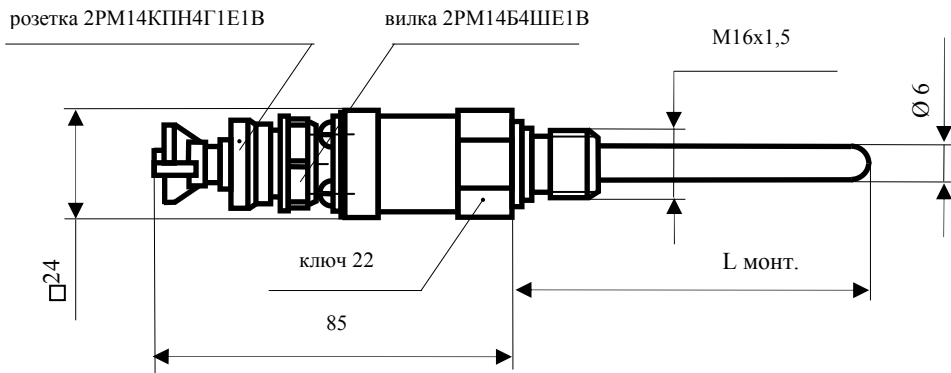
Габаритные и присоединительные размеры ТСП 002-05 модель 2
